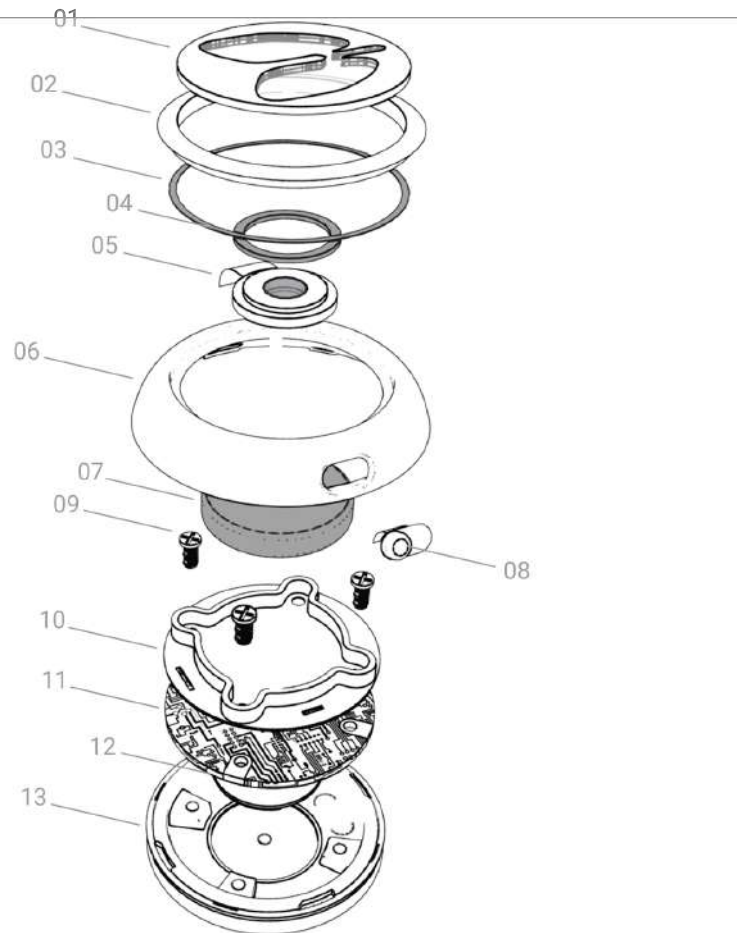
Ilustración explosivo del sensor de esfuerzo respiratorio.
